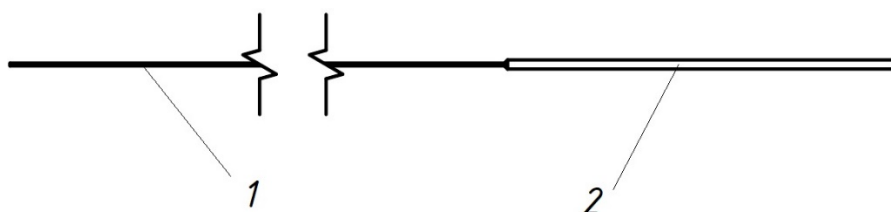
Схема конструкции микрошлифовального инструмента для обработки отверстий и углублений: 1 – крепежная часть; 2 – рабочая часть
